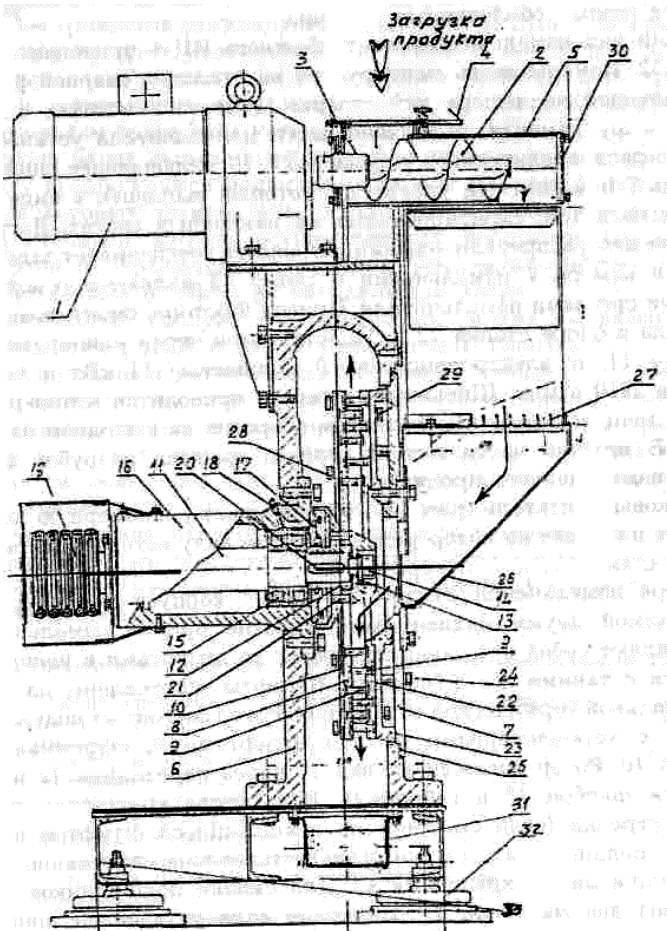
Центробежный измельчитель ИЦ-1: 1 — мотор-редуктор; 2 — шнек питателя; 3 — втулка; 4 — задвижка; 5 — корпус шнека; 6 — корпус; 7 — откидная дверка; 8 — диск ротора; 9 — пальцы (штифты); 10 — шайба; 11 — вал ротора; 12 — переходник; 13 — шайба; 14 — гайка; 15 — роликовый подшипник; 16 — стакан (опора); 17 — крышка; 18 — масленка; 19 — шкив; 20 — шпонок; 21 — штифт; 22 — неподвижный диск с пальцами (штифтами); 23 — диск; 24, 28, 29 — болт; 25 — резиновый шнур; 26 — загрузочный патрубок; 27 — решетка; 30 — стенка шнека; 31 — патрубок вывода измельченного продукта; 32 — виброопора; 33 — опорная рама
